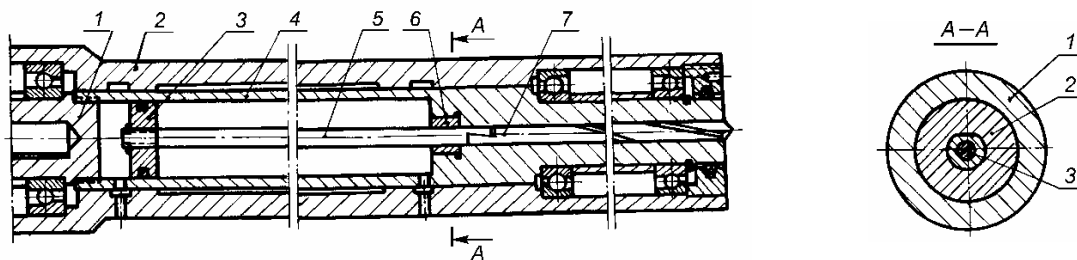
Механізм приводу верстатів для глибокого свердління
